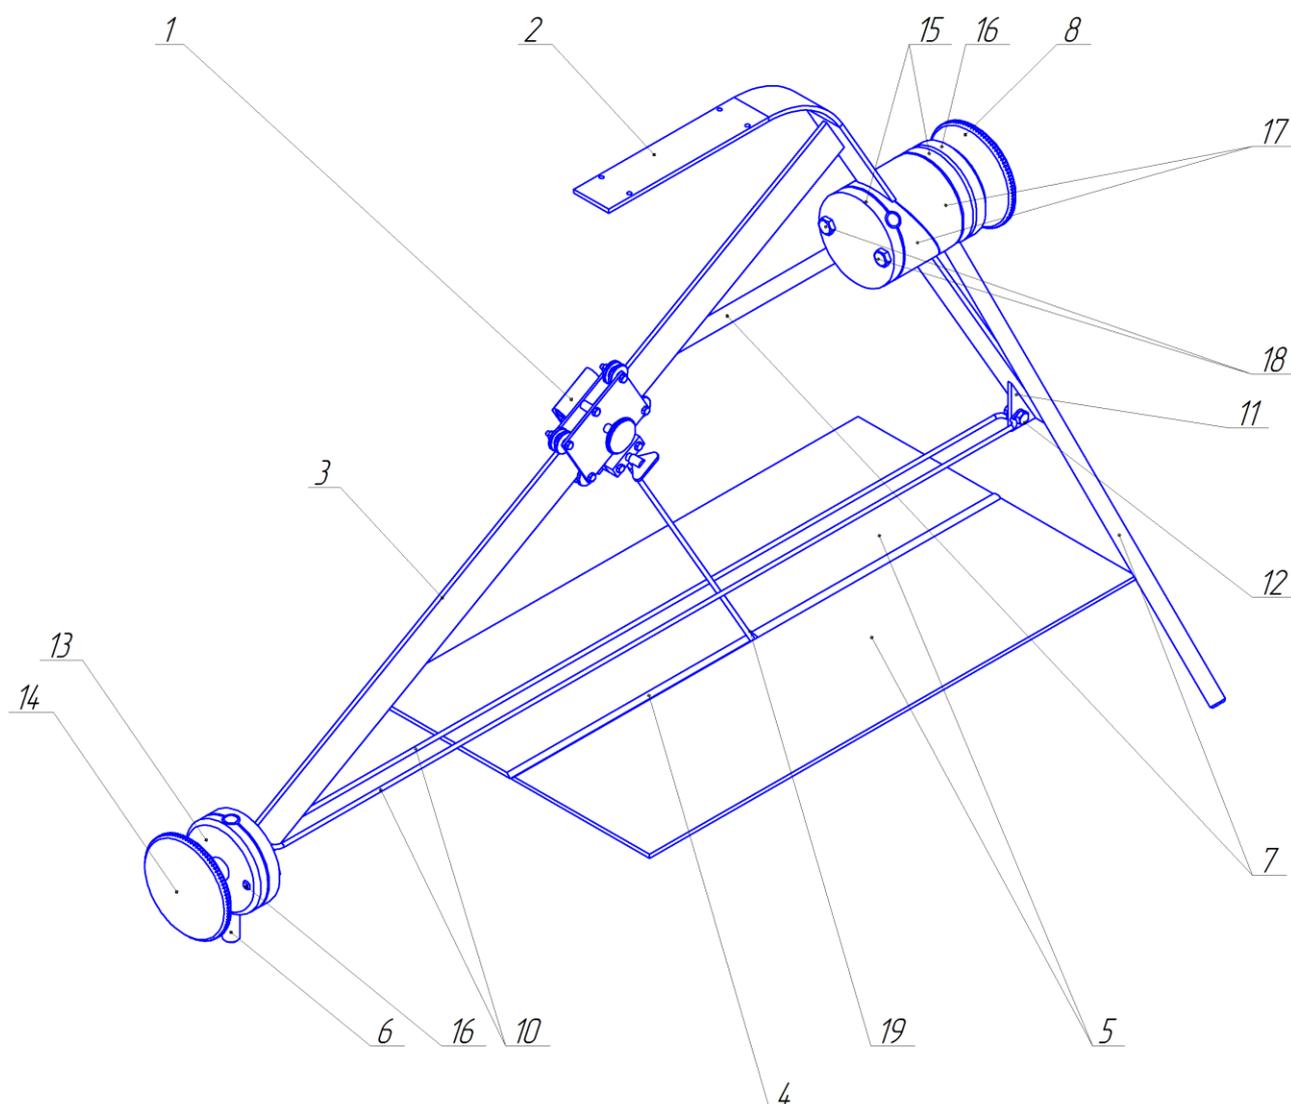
Изометрический вид конструкции установки для гравитационной сварки
